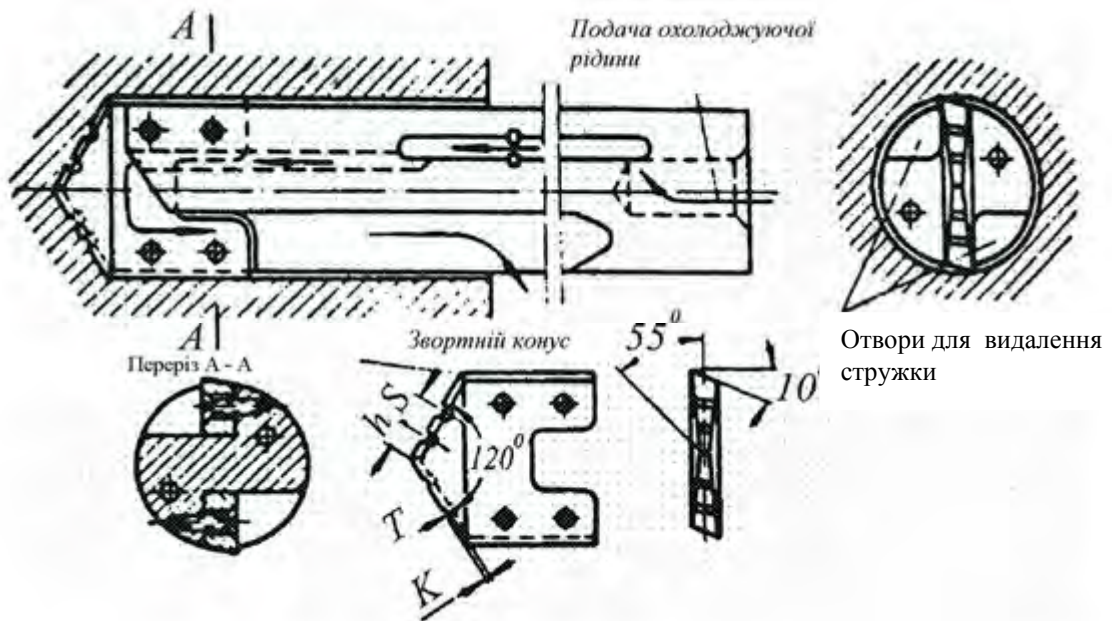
Свердло з двома кромками для глибокого свердління з полішеними умовами центрування
